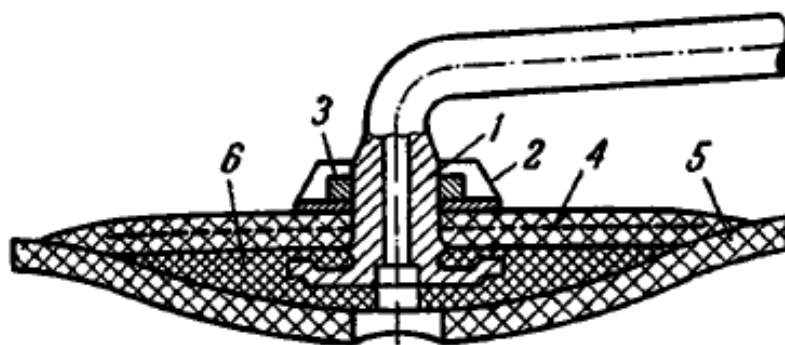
Резино-металлический вентиль для шин легковых автомобилей
